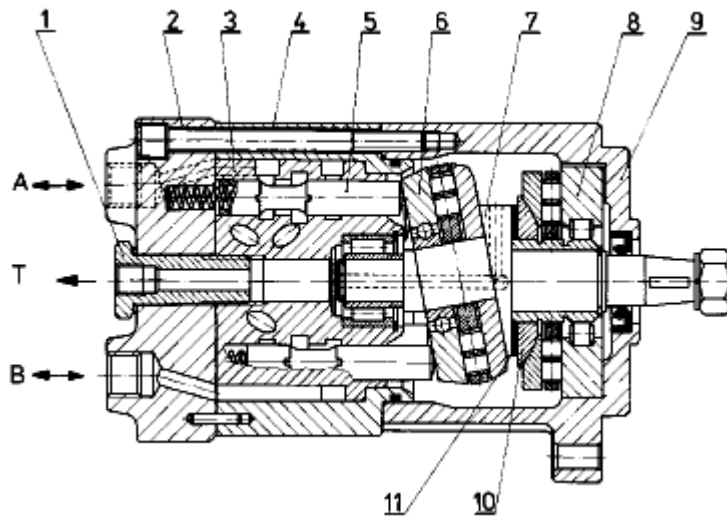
Motor cu pistoane axiale și disc oscilant:
